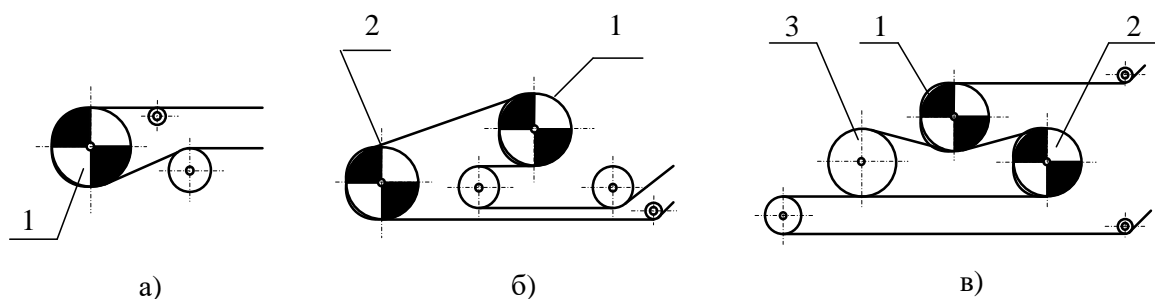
Приводи конвеєрів: а) – однобарабанний; б) – двобарабанний; в) – багатобарабанний
